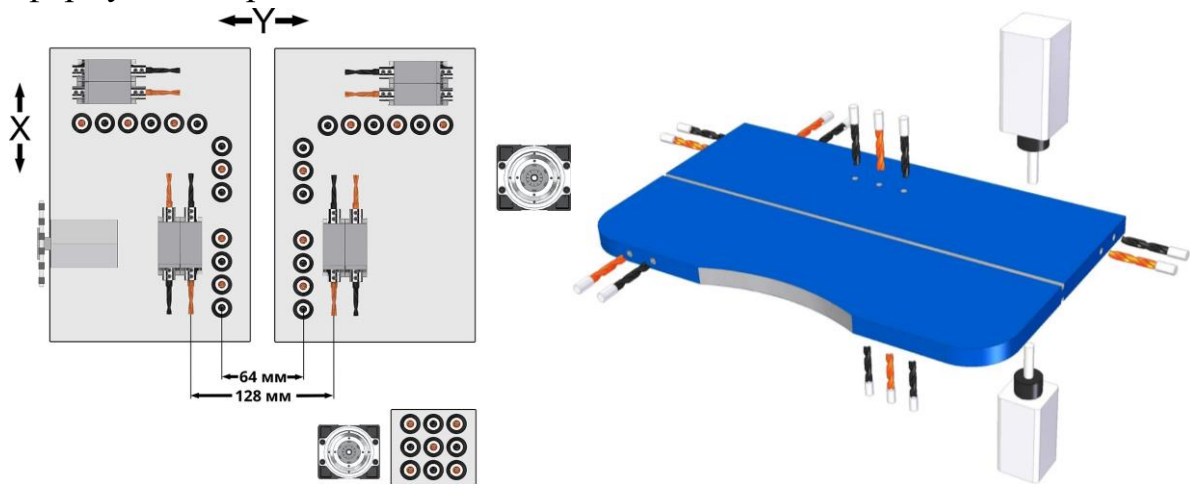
Схема свердлильних груп та схема обробки деталей на горизонтальних свердлильно-присаджувальних центрах з ЧПК
